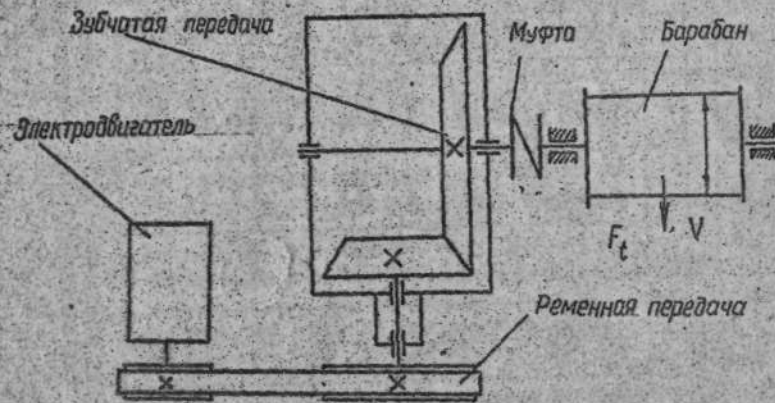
Схема привода ленточного транспортера для выдачи багажа в аэровокзалах
